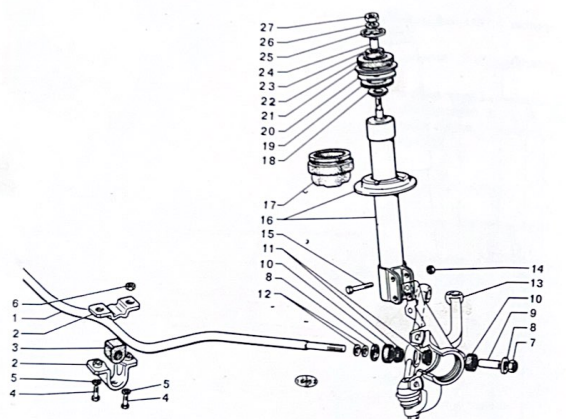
Despiece de amortiguador delantero y barra estabilizadora.
